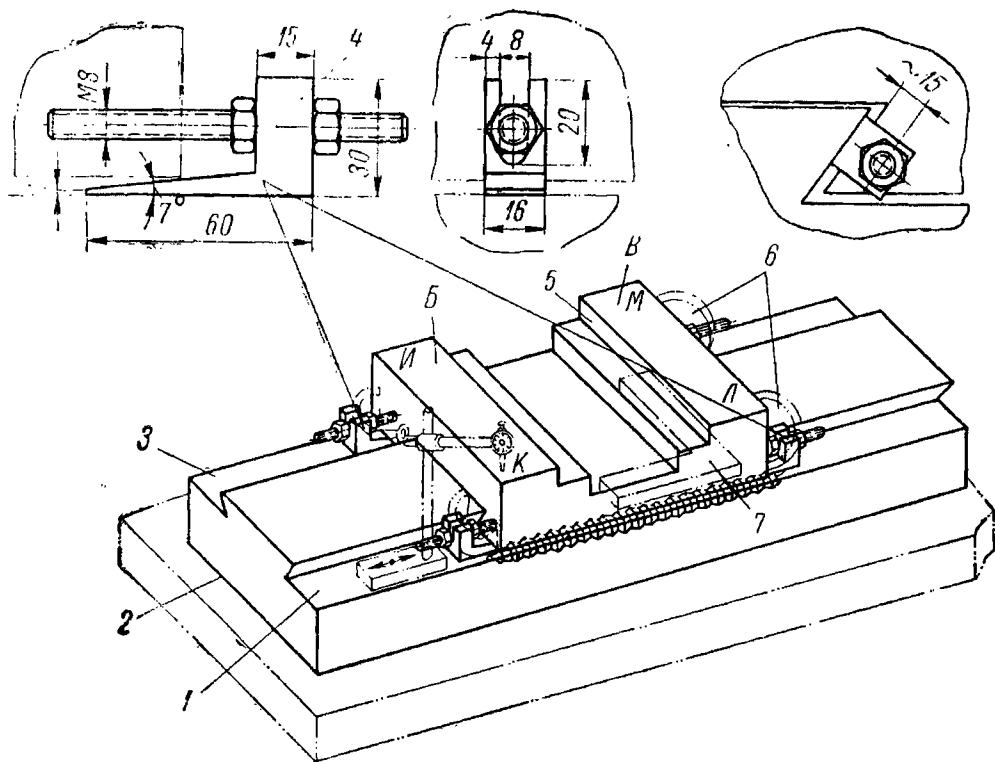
Подготовка каретки для восстановления верхних направляющих
